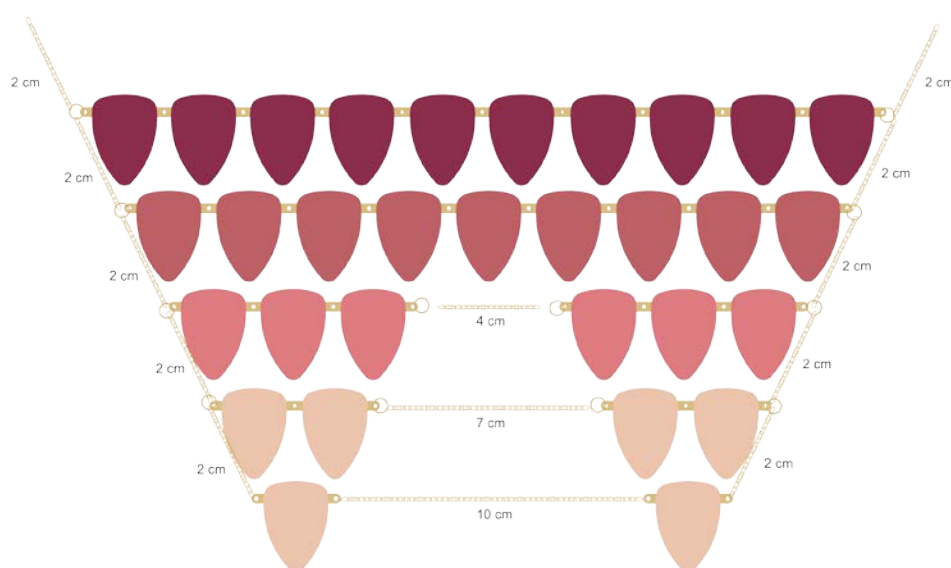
Desenho esquemático de montagem de montagem do colar do conjunto 2
